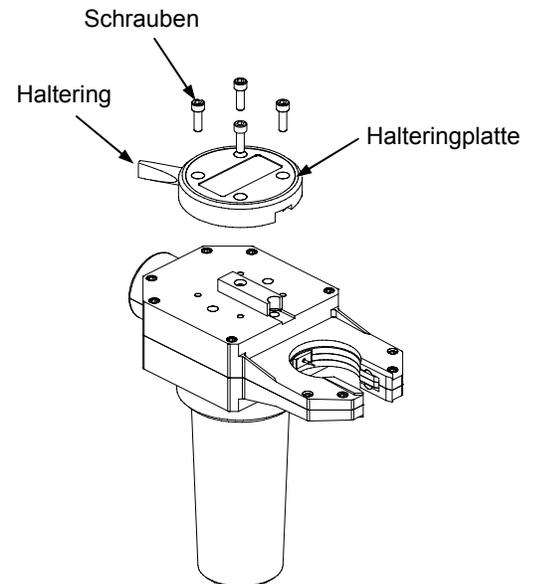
Entfernen des Halterings und der Halteringplatte
